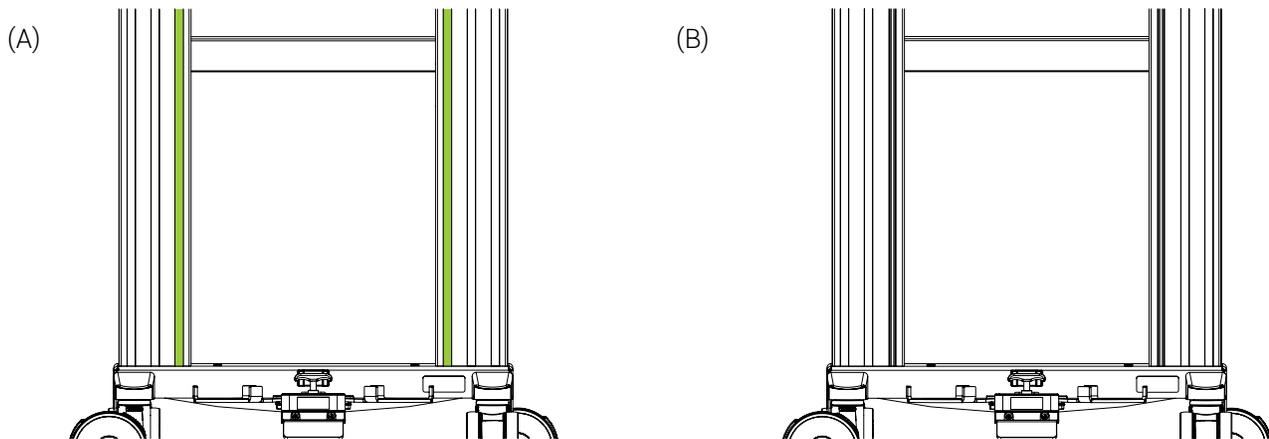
Pièces d'assemblage du support pour cylindres à gaz
